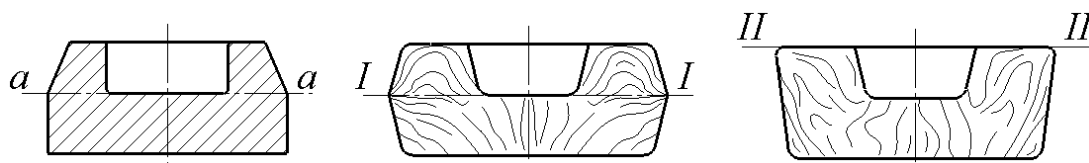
Вибір поверхні розняття штампа за умовами роботи деталі
